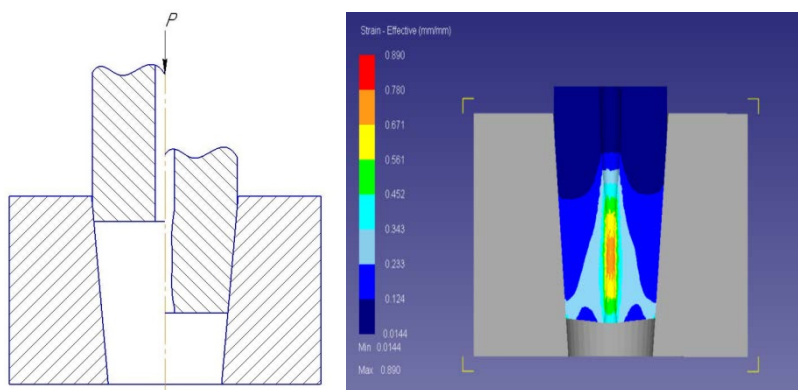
Схема процесса обжатия (а) и напряженное состояние (б) цилиндрической заготовки
